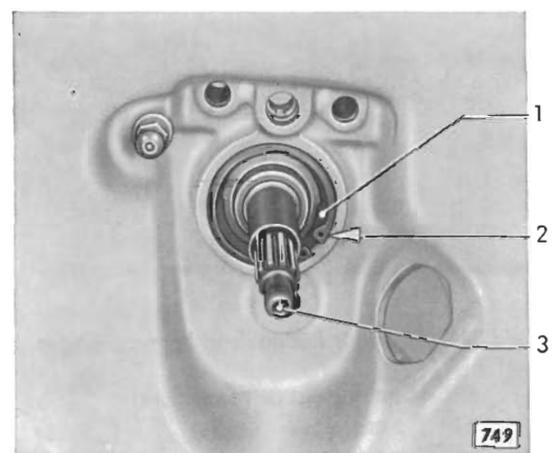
Hauptantriehrad in Getriebegehäuse eingebaut
